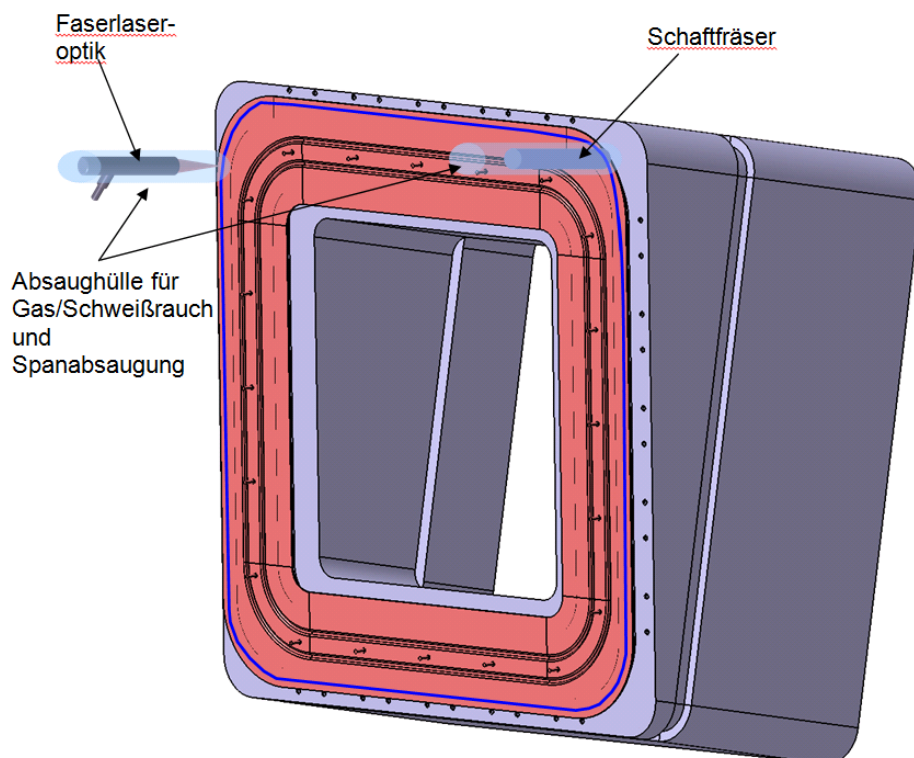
Schematische Darstellung der Schweiß- und Fräsvorrichtung an der Port-Plug Dichtung mit umhüllender Absaugvorrichtung für Gas-/Schweißrauch und Metallspäne
